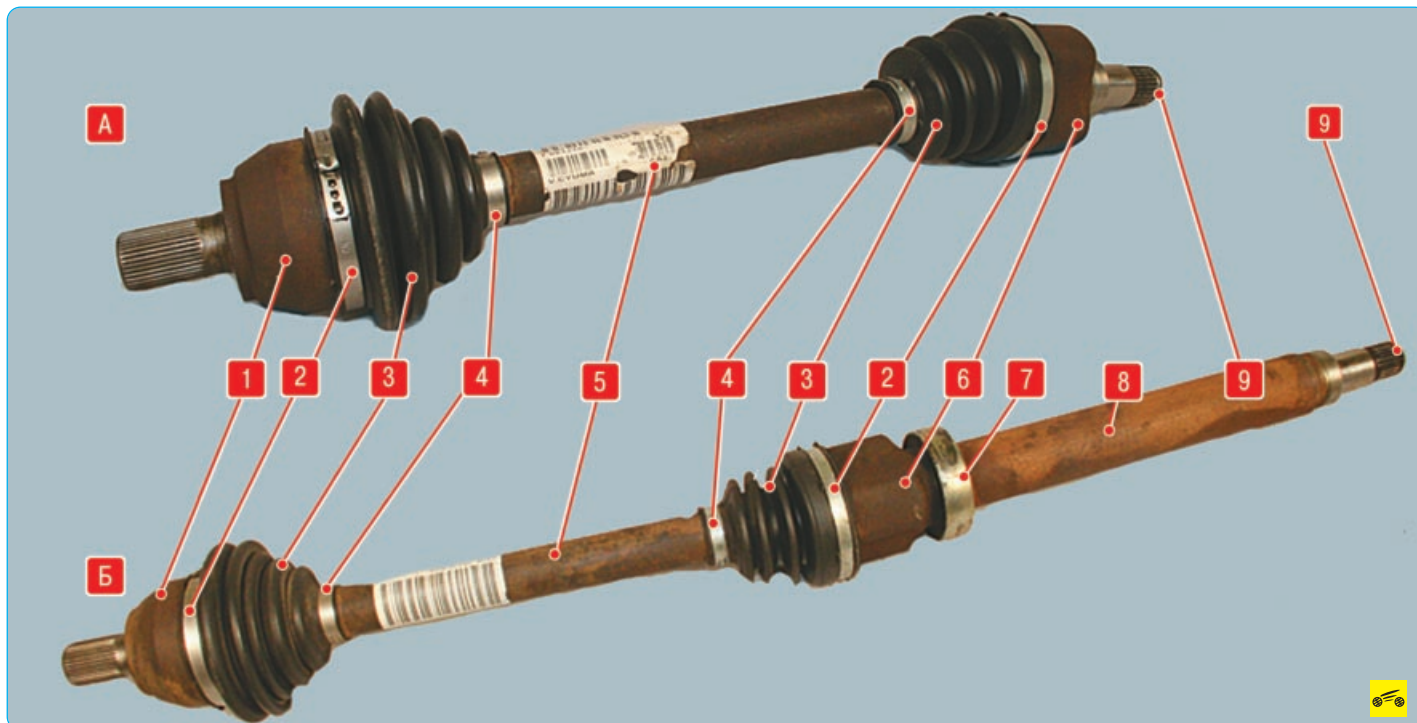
Приводы передних колес: А – привод левого переднего колеса; Б – привод правого переднего колеса; 1 – наружные шарниры равных угловых скоростей; 2 – большие хомуты крепления чехлов шарниров; 3 – чехлы шарниров; 4 – малые хомуты крепления чехлов шарниров; 5 – валы приводов; 6 – внутренние шарниры равных угловых скоростей; 7 – подшипник промежуточной опоры; 8 – промежуточный вал; 9 – стопорное кольцо
